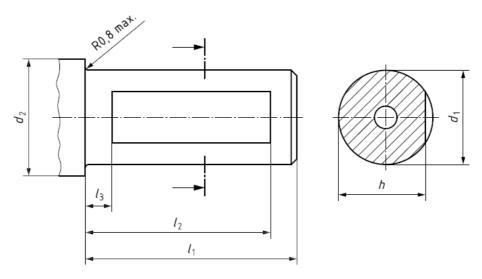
Пример цилиндрического хвостовика с параллельной лыской для сверл со сменными режущими пластинами
